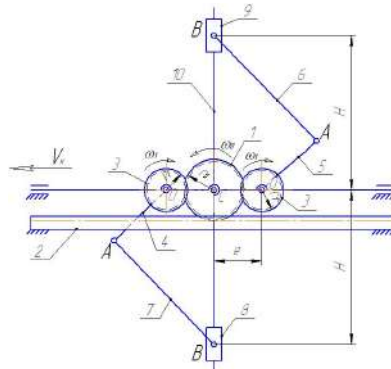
Схема механізму привода вузла поперечного зварювання плівки:
